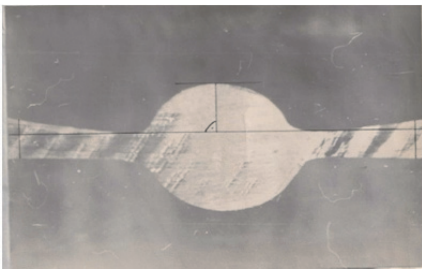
Поперечное сечение контрольной поковки после изготовления 1100 деталей, образец №1'
